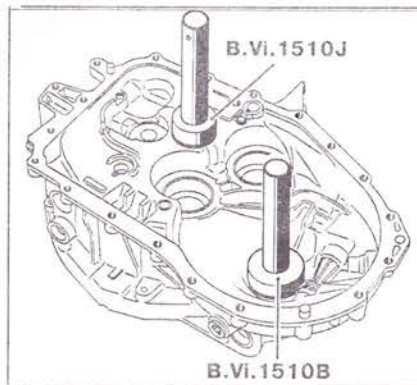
Установите опоры подшипников валов при помощи приспособлений В. Vi. 1510J и В. Vi. 1510B.
